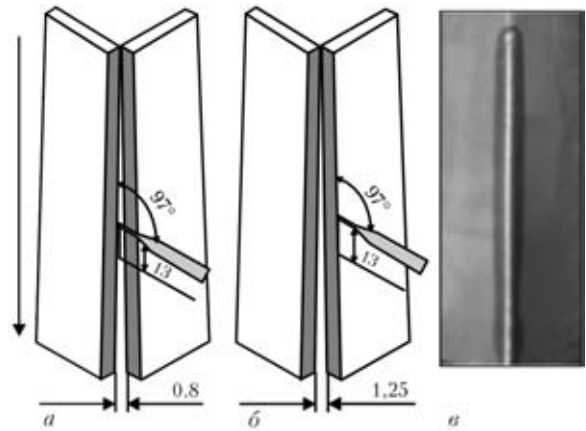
Выполнение модифицированной МАГ сварки при увеличивающемся зазоре в корне (а, б) и внешний вид соединения (в)
